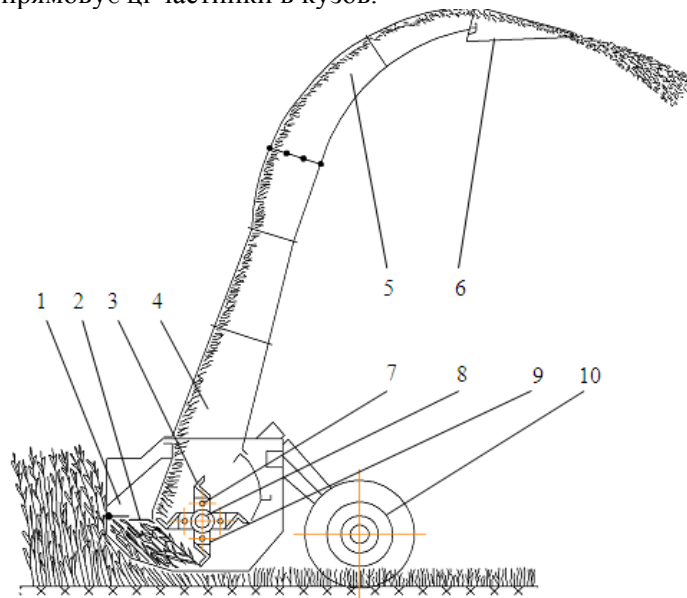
Технологічна схема машини КІР-1,5: 1-кожух; 2-протиризальний упор; 3-ніж; 4-вивантажувальний розтруб; 5-поворотний розтруб; 6-дефлектор; 7-шарнір; 8-трубчастий вал; 9-кронштейн-тримач; 10-колесо
